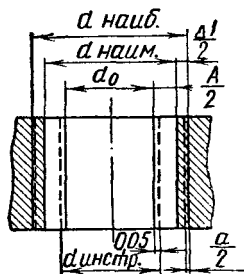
Расположение полей допусков и припуск на протягивание
